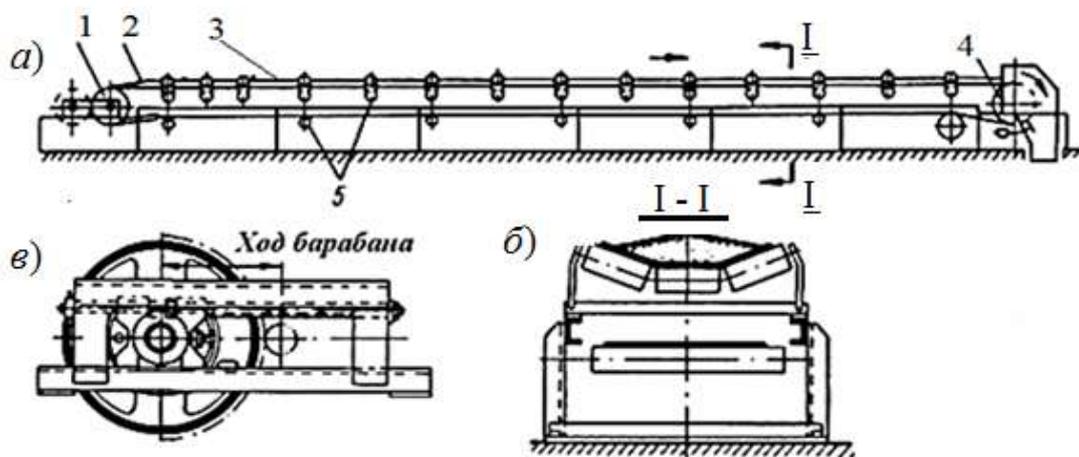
Ленточный конвейер: а - схема стационарного горизонтального конвейера; б - поперечный разрез; в - натяжное устройство; 1 – натяжной барабан; 2 – лента; 3 – загрузочный бункер; 4 – приводной барабан; 5 – роликовые опоры.
